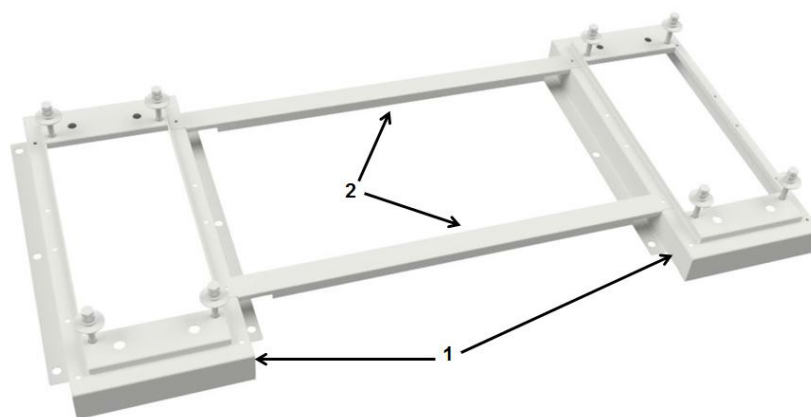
Samlet fixtur monteret med afstandsskiner
